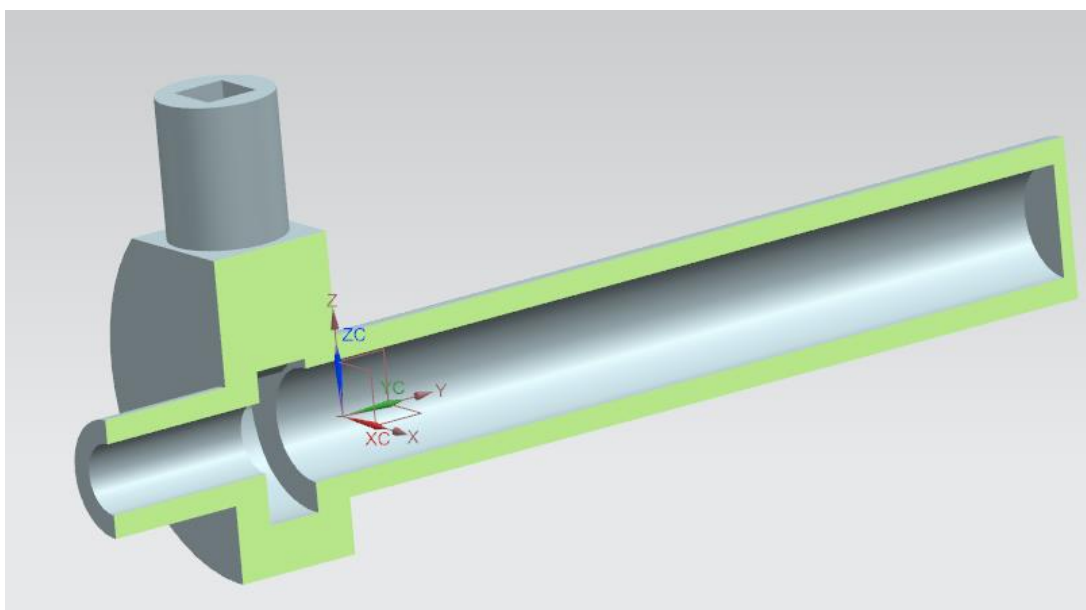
Вид детали в разрезе после создания канала трубы
